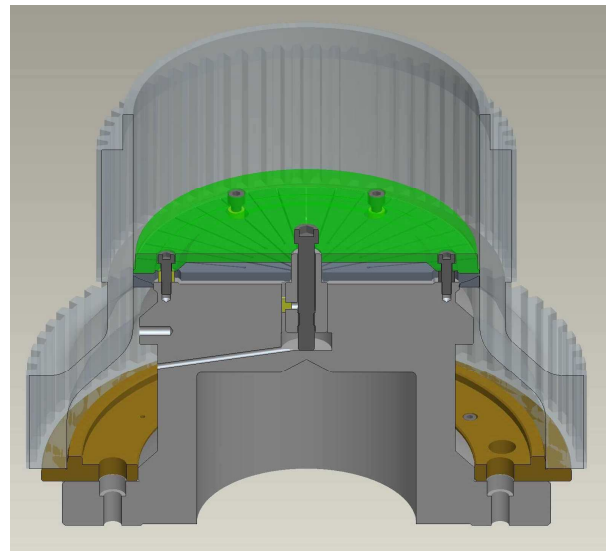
Flachdorn-Spannzeug für Getriebeglocke in 3 D Darstellungen
